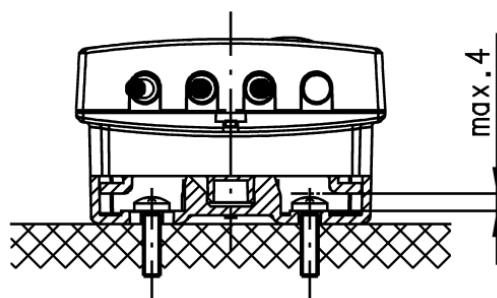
Maks høyde på skruehode ved bruk av brakett
